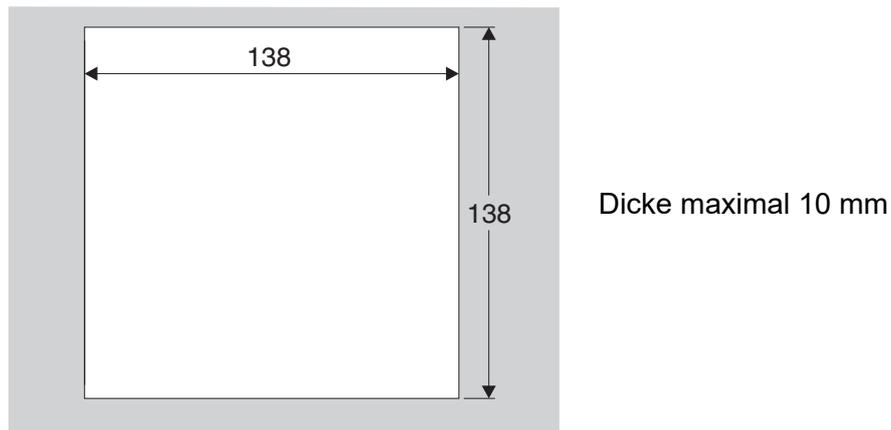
Montageöffnung in der Schalttafel (Maße in mm)
